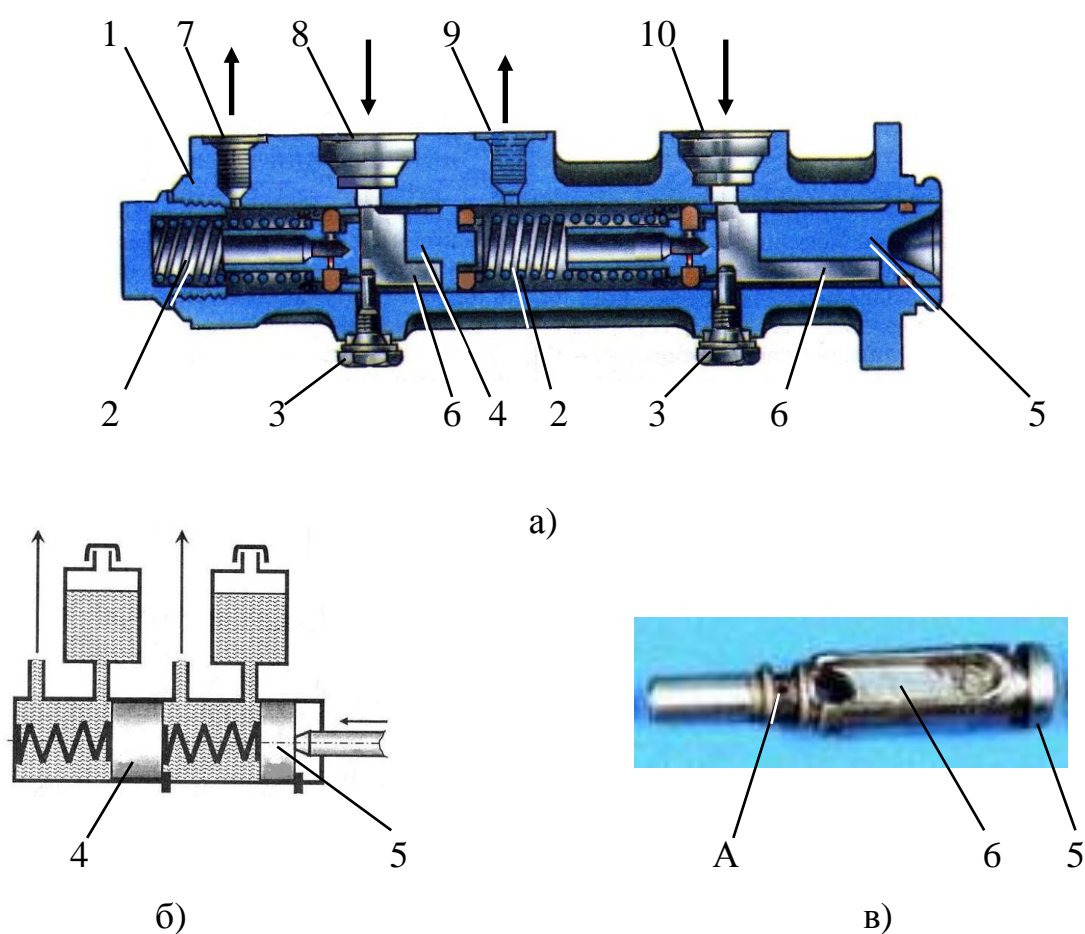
Главный тормозной цилиндр: а – конструкция, б – схема работы, в – поршень главного тормозного цилиндра; 1 – корпус цилиндра; 2 – возвратные пружины; 3 – упорные винты; 4 – поршень привода второго тормозного контура; 5 – поршень привода первого тормозного контура; 6 – пазы поршней; 7 – выход на второй тормозной контур; 8 – вход из передней секции дополнительного бачка; 9 – выход на первый тормозной контур; 10 – вход из задней секции дополнительного бачка; А – радиальное отверстие в канавке поршня
